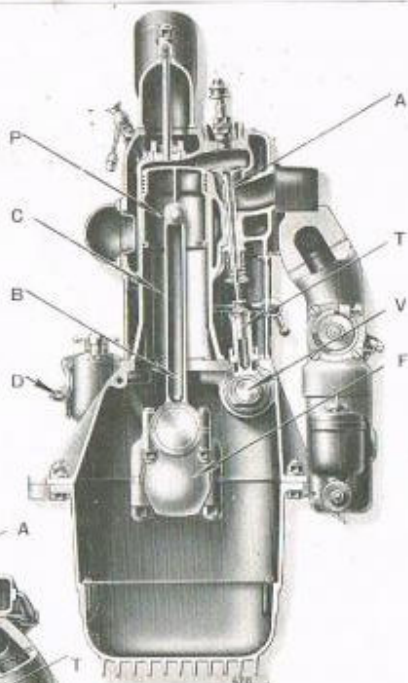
Coupe transversale du moteur 18 CV, par l'axe d'un cylindre.
